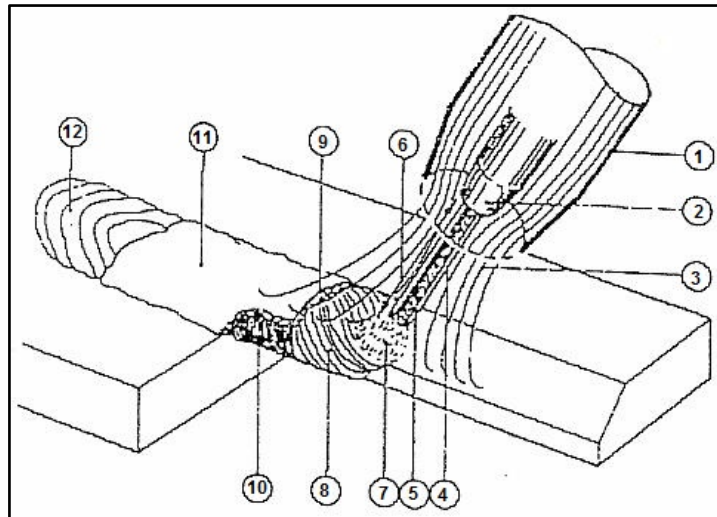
Soldadura MIG para acero inoxidable [12]
